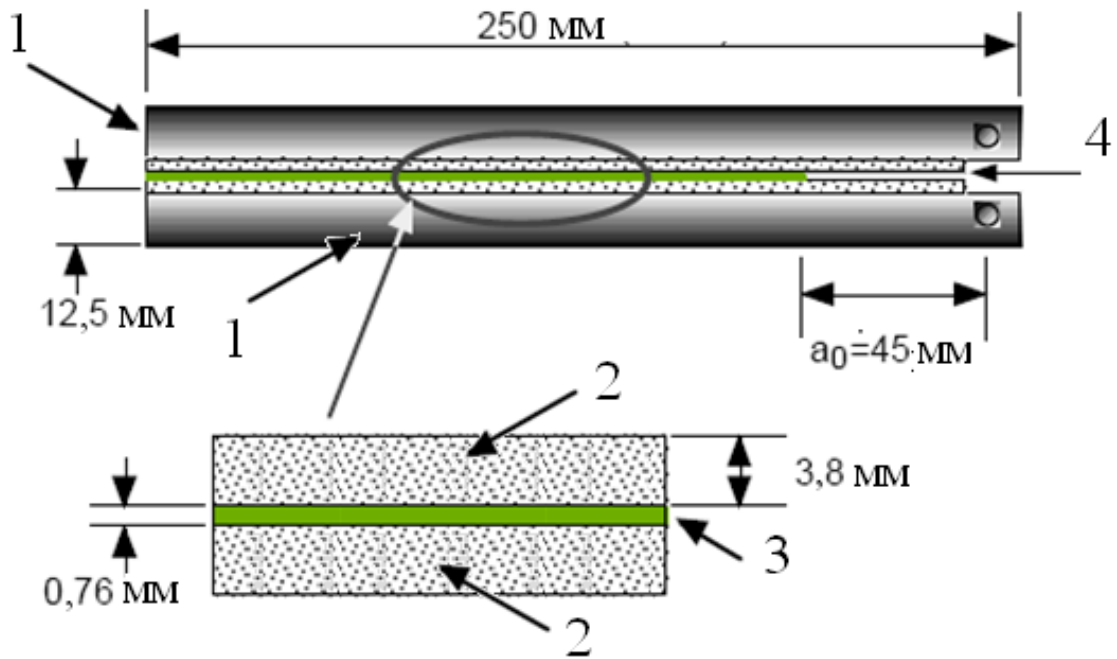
Схематичне зображення DCB зразка [264]: 1 – алюмінієві листи; 2 – композитна плита; 3 – клейовий шар; 4 – початок тріщини
